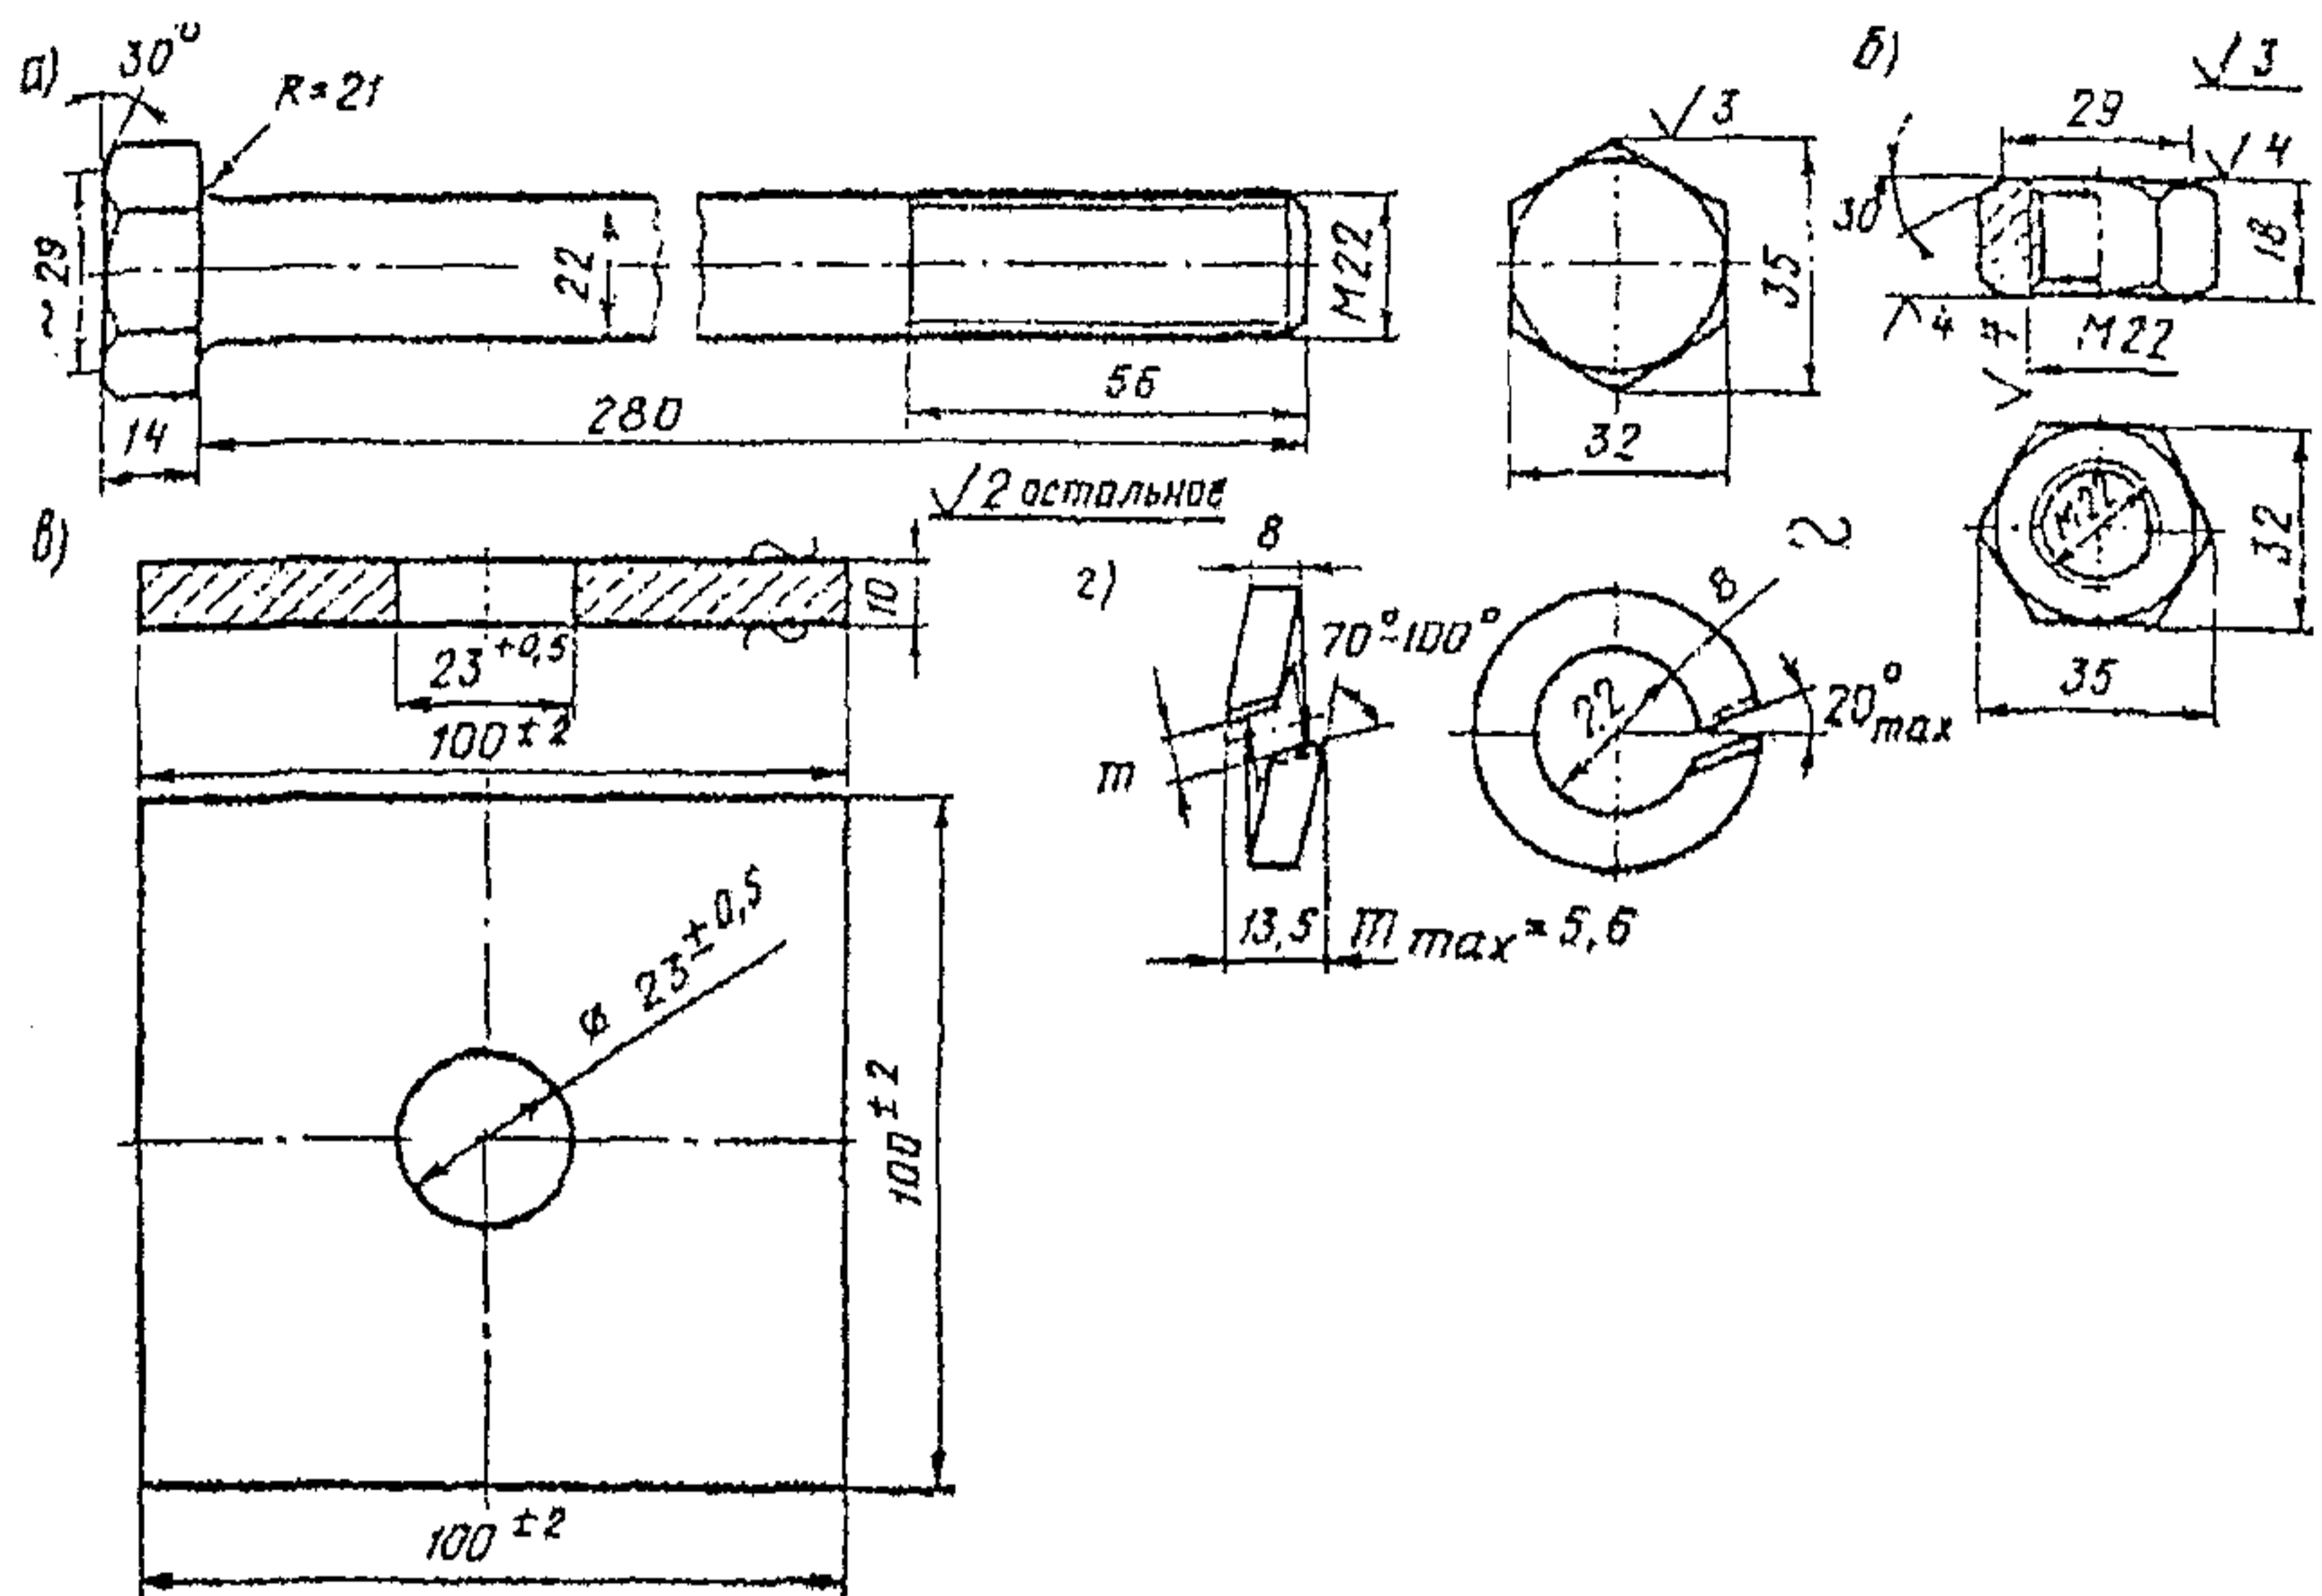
Болт для прикрепления контруголка к безбалластным железобетонным плитам:
